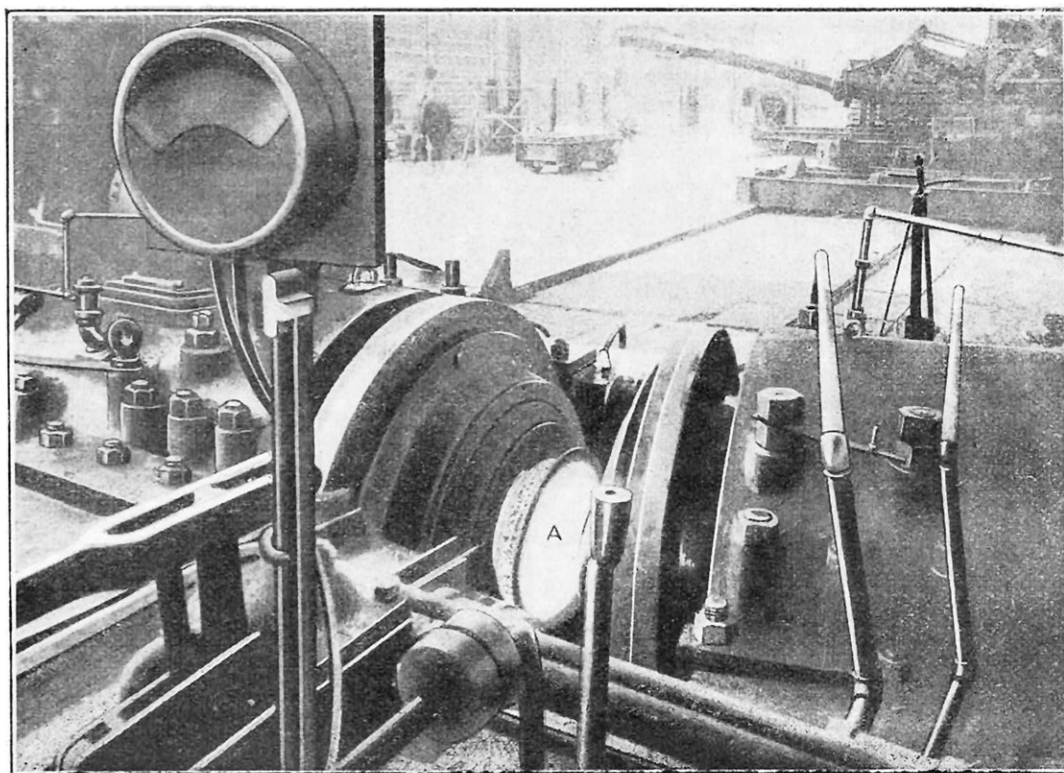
VUE DES DISQUES AU MOMENT OU LA ROUE (A) SORT DE LA MACHINE
